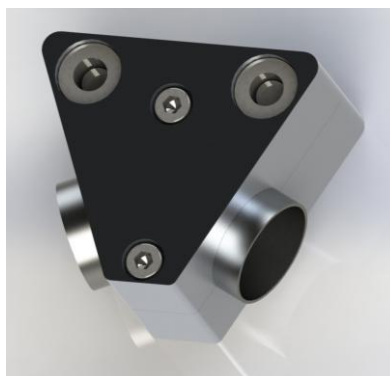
Utillaje de posicionamiento para soldeo de tubo de salida de gases.
